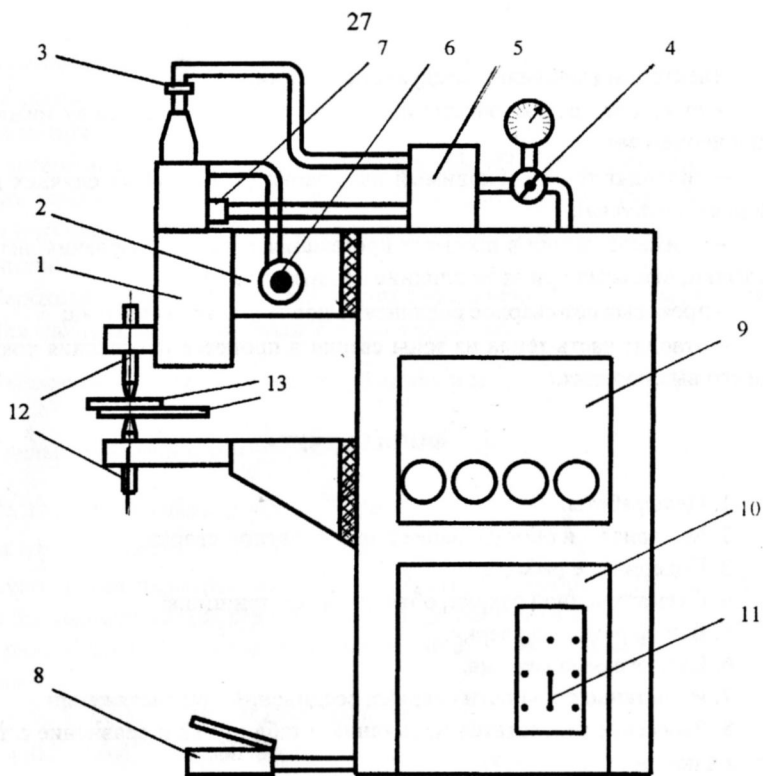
Типовая схема машины для точечной сварки:
